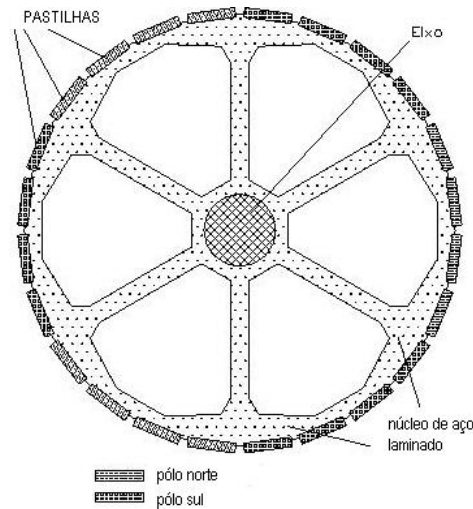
Corte transversal de um rotor de 6 pólos com ímã permanente montado na superfície do rotor.
